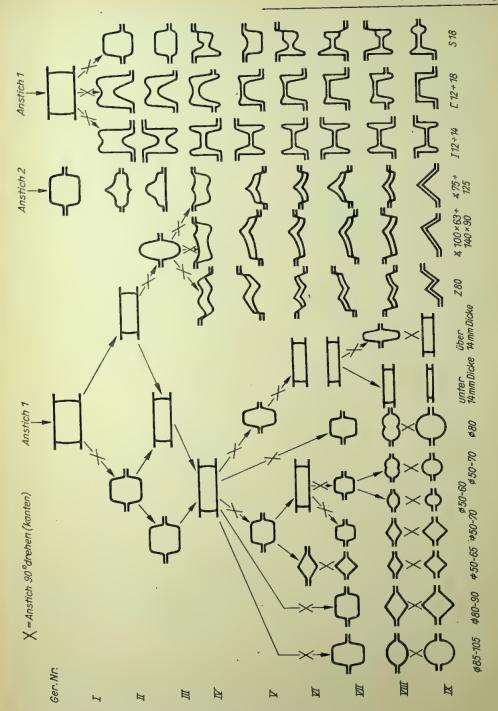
Kalibrierung und Walzplan einer Mittelstraße für Profile
